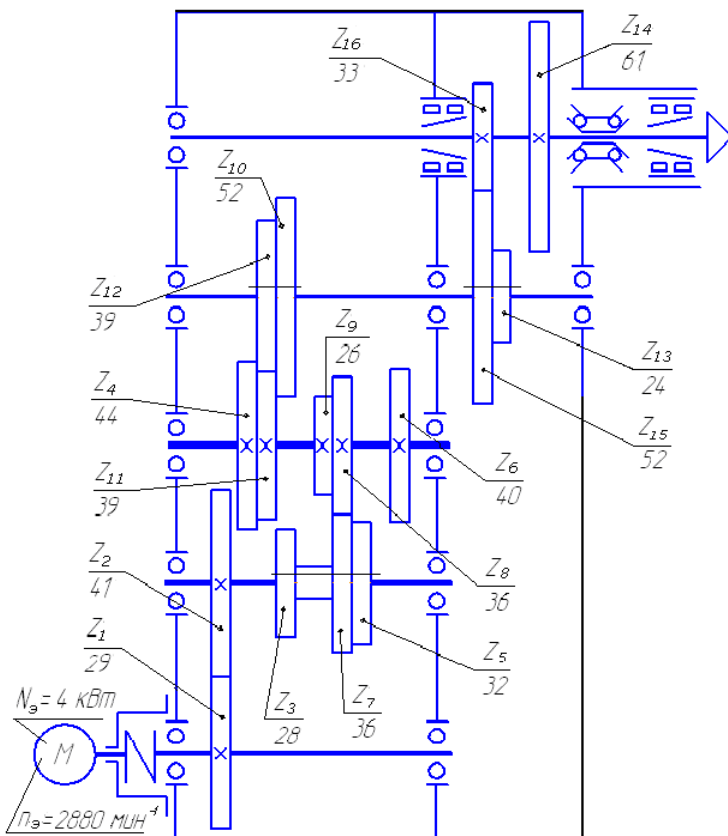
Кинематическая схема главного привода горизонтального консольно-фрезерного станка
